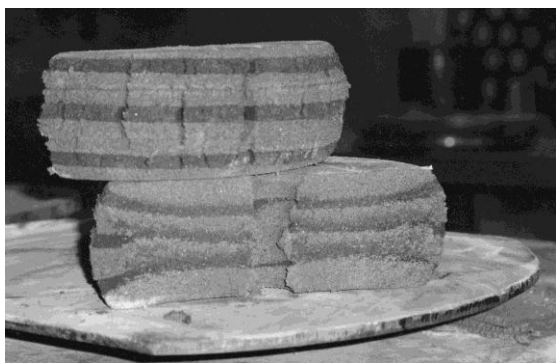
Боковая поверхность с разрывами и сечение образца, осажденного между сухими металлическими плитами
